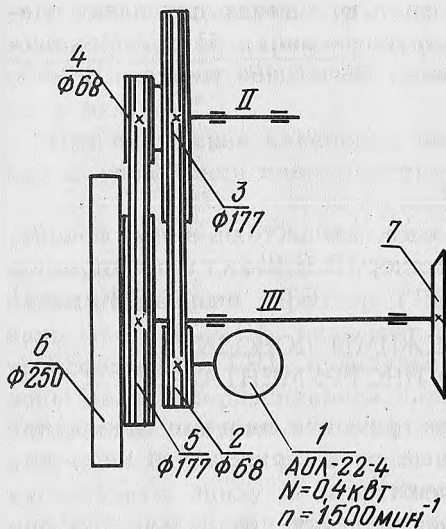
Кинематическая схема установки для доводки инструмента на базе станка ЗВ642.
